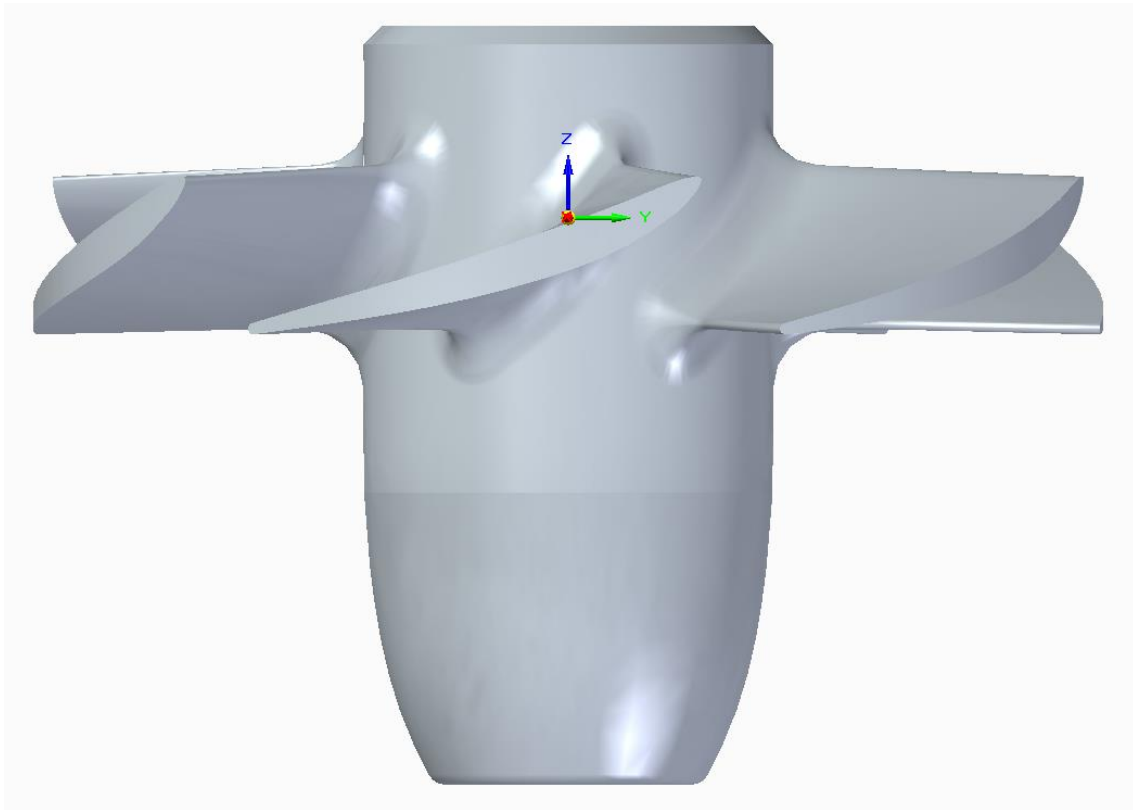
Vista de alzado del rodete acabado. (Elaboración propia)
